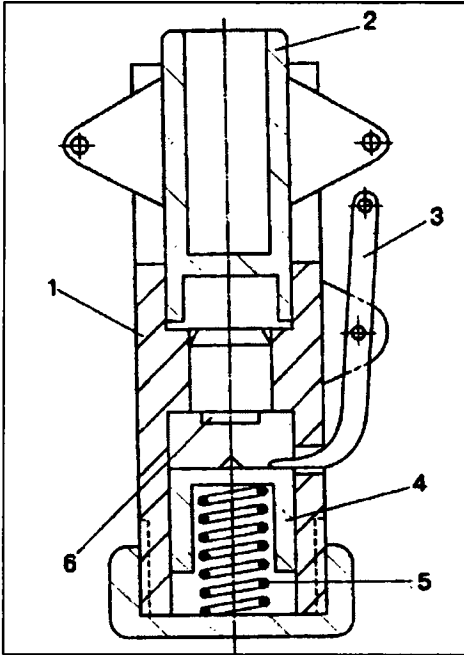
Пиротехническое устройство для вскрытия разрывного: 1 — корпус; 2 — груз; 3 — рычаг; 4 — боек; 5 — пружина; 6 — поршень
